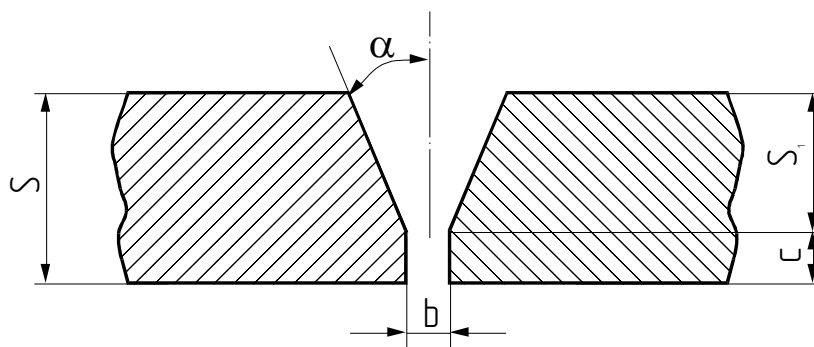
Разделка кромок под сварку стыковых швов
